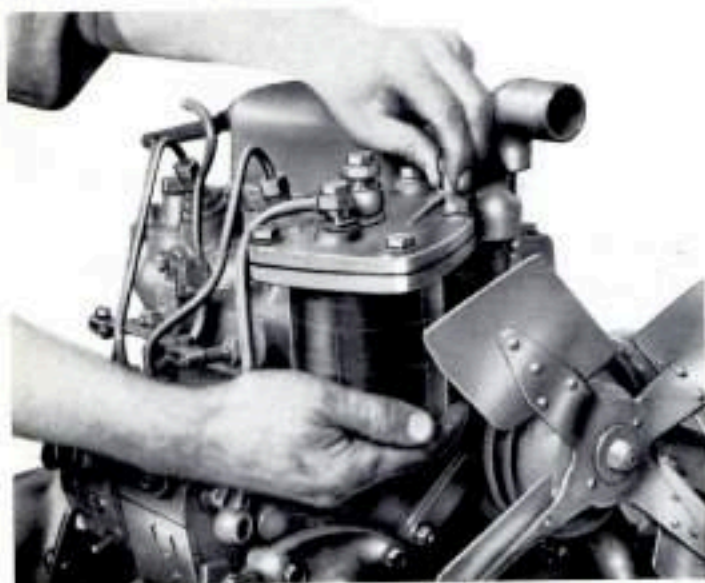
Smontaggio del motore: viene asportato il filtro gasolio.
